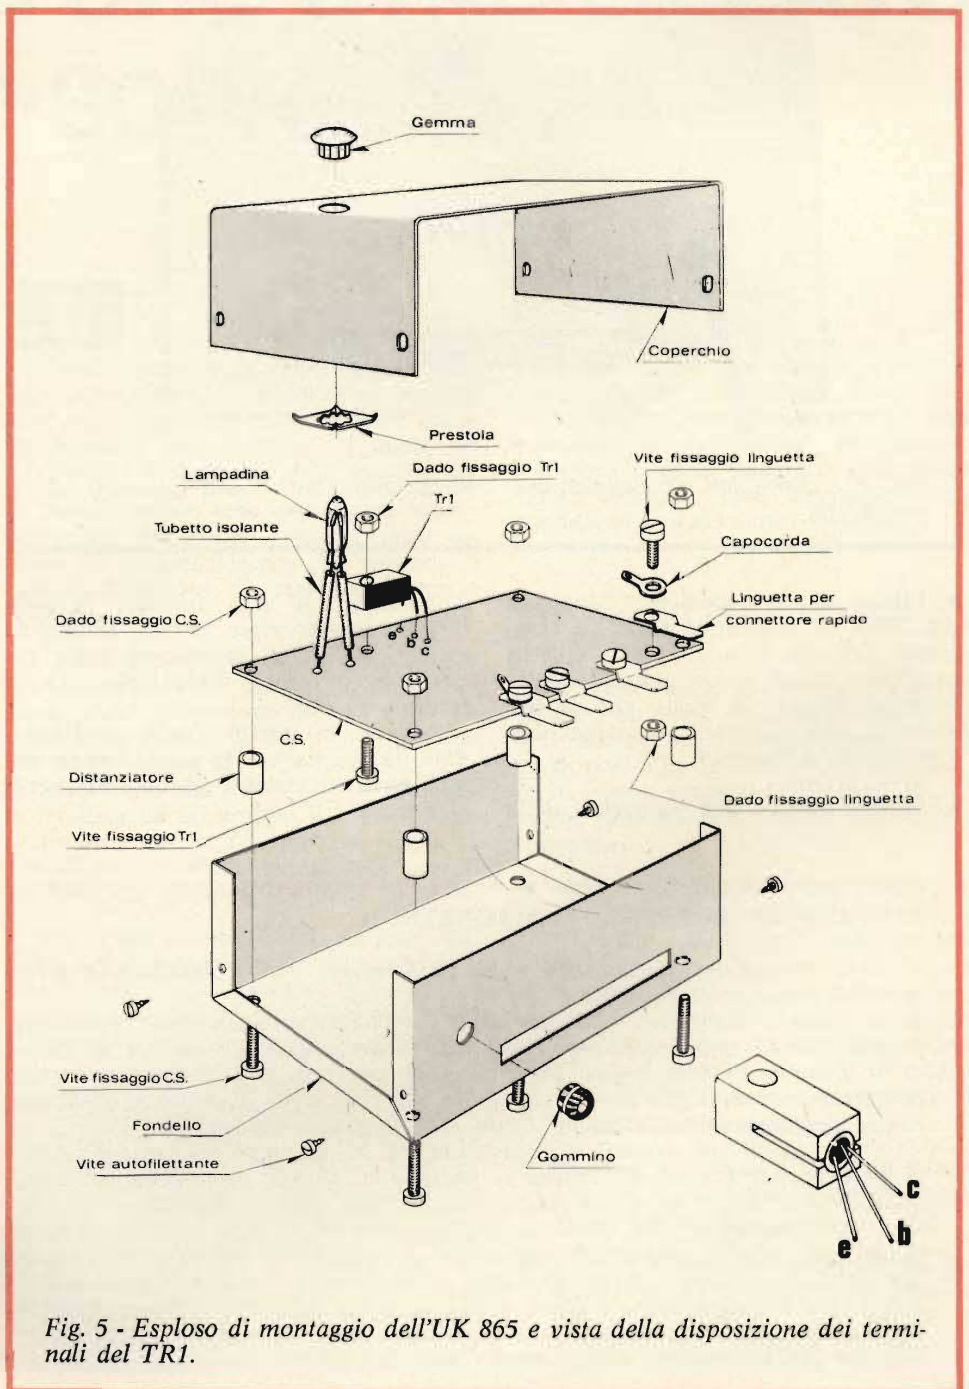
Esploso di montaggio dell'UK 865 e vista della disposizione dei terminali del TR1.
